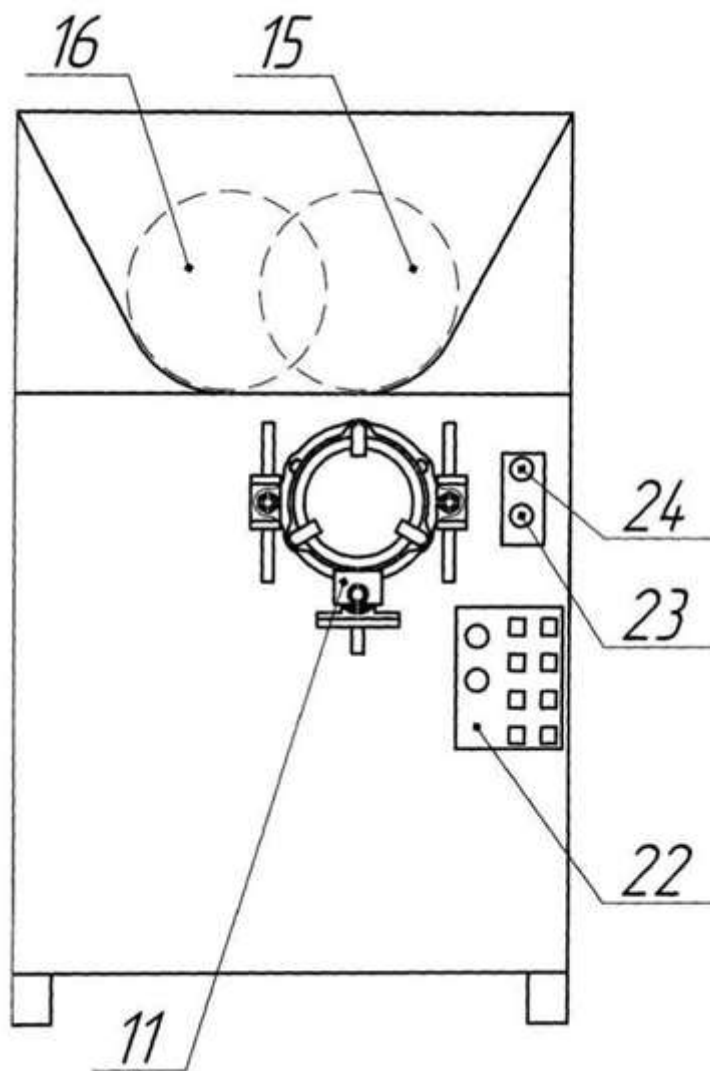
загальний вигляд вовчка (вид спереду)
